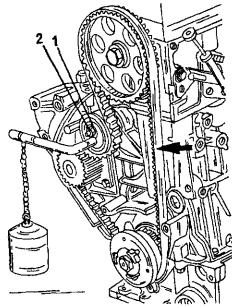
Устройство для натяжения зубчатого ремня, смонтрованное на натяжном ролике.
